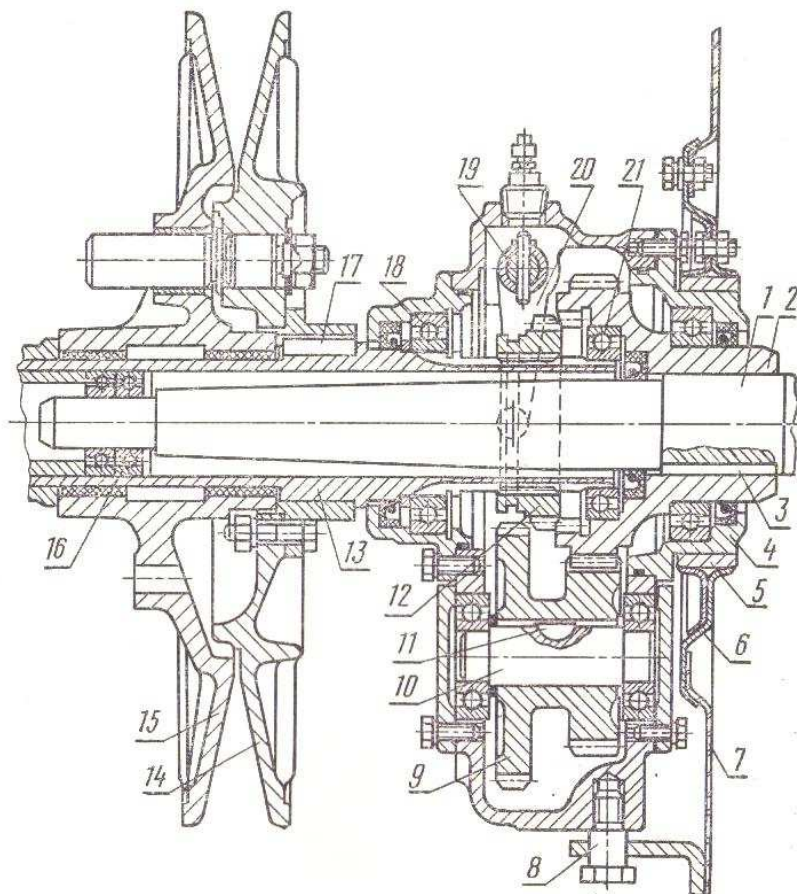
Редуктор привода барабана комбайна СК-6: 1 – вал; 2 – ведомая шестерня редуктора; 3 – шпонка; 4 – корпус; 5 – сферическое кольцо; 6 – разъемная обойма; 7 – панель корпуса молотилки; 8 – стопорный болт; 9 – блок шестерен; 10 – ось блока шестерен; 11 и 17 – шпонки; 12 – ведущая шестерня; 13 – трубчатый вал; 14 – неподвижный диск; 16, 18, 21 – подшипники; 19 – валик вилки; 20 – вилка
